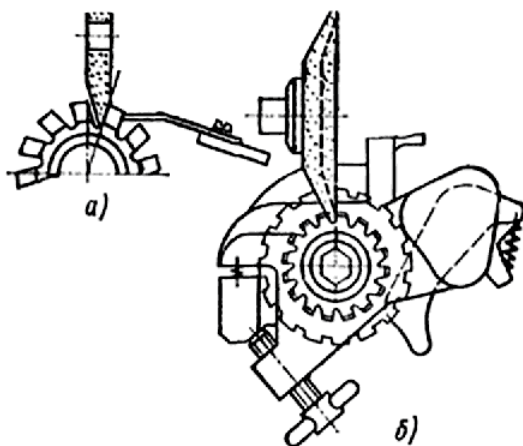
Схемы фиксации фрезы при заточке по передней поверхности с помощью упорки (а) или делительного приспособления (б)
